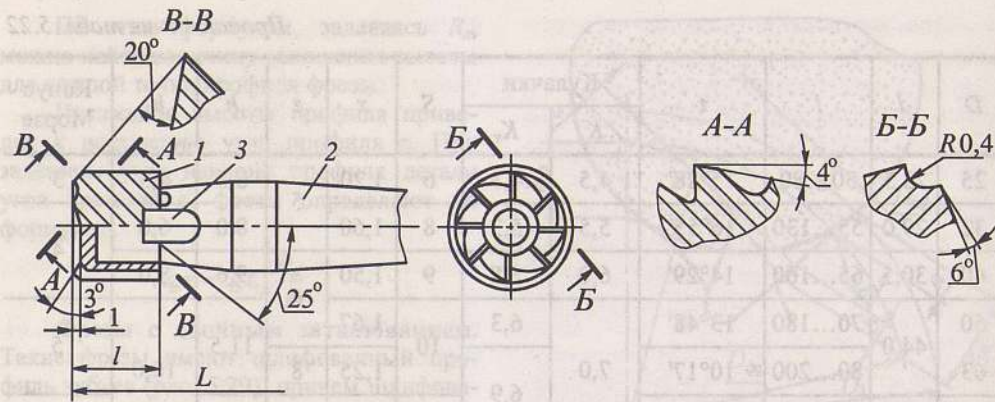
Фреза концевая, оснащенная монолитной коронкой из твердого сплава:
